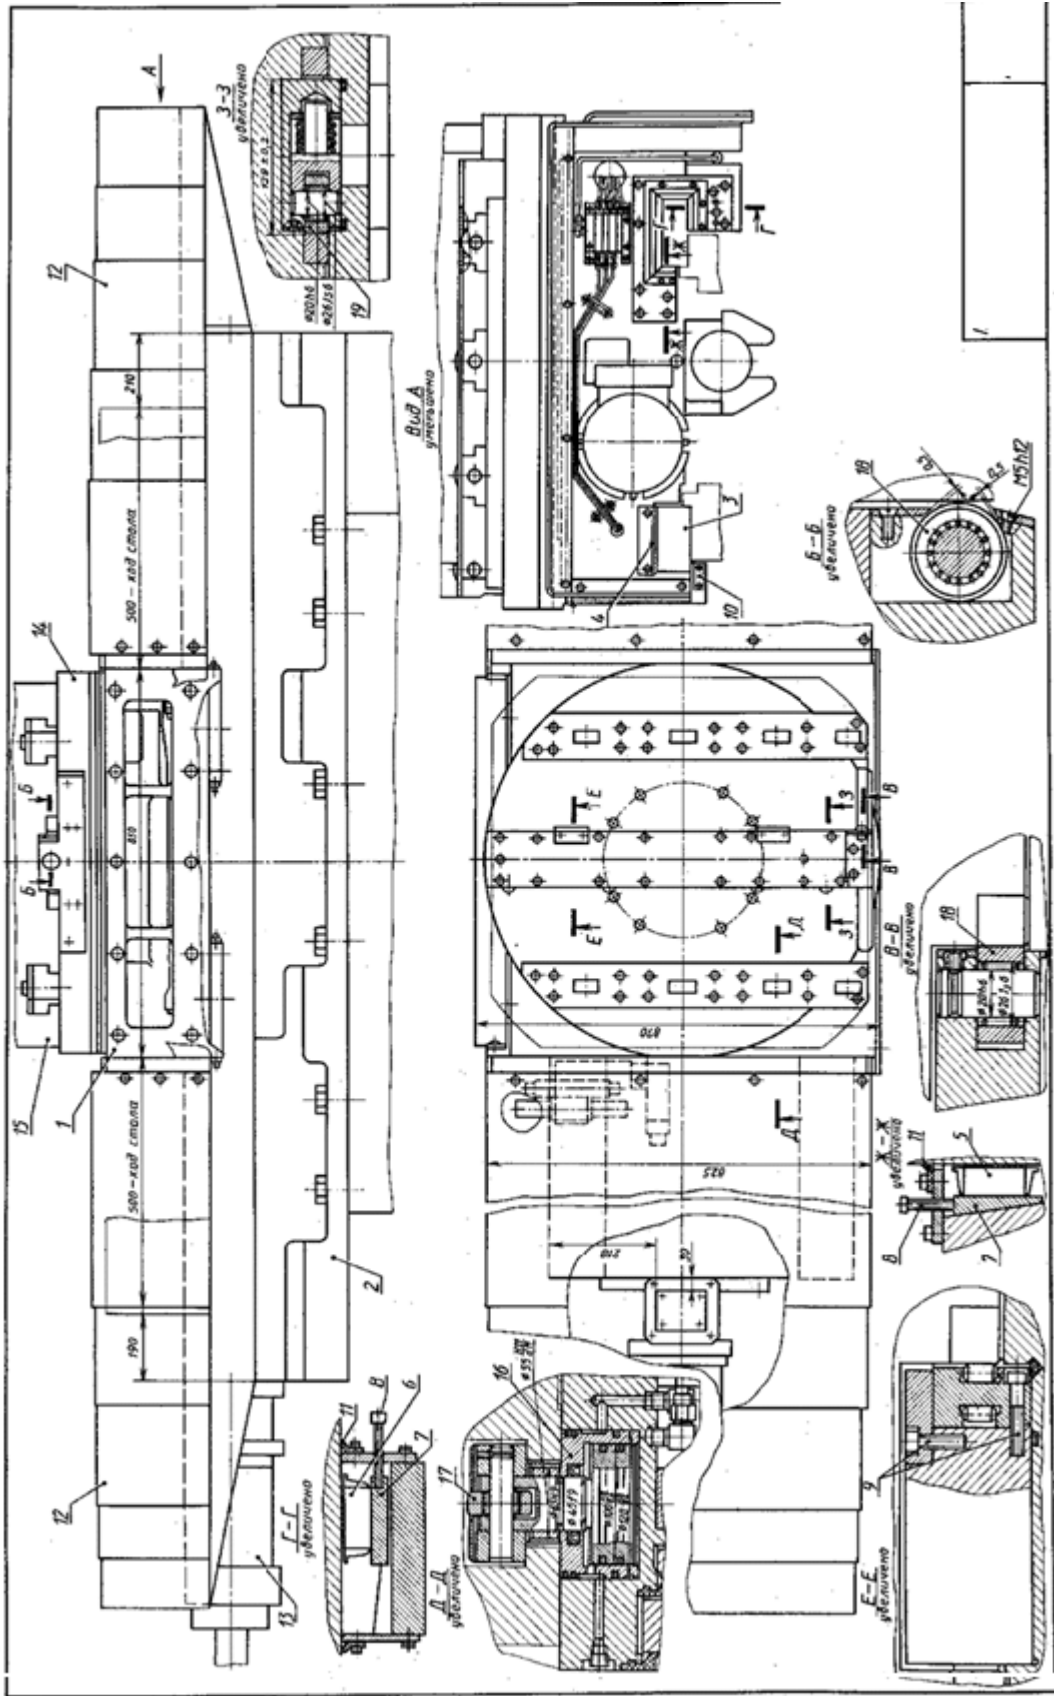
загальний вид і конструкції поперечно-рухливого і поворотного столів верстата мод. IP800ПМФ4
